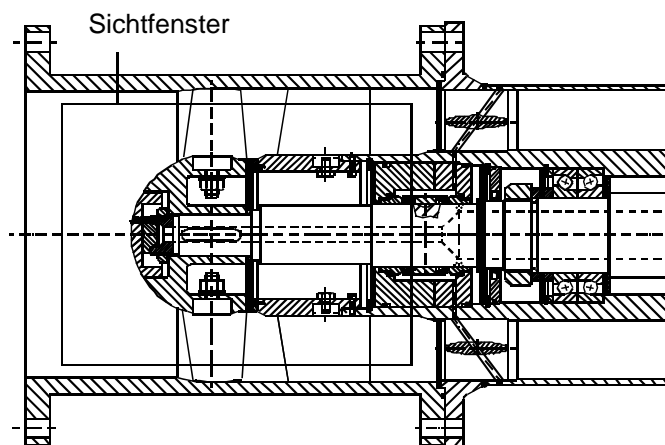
Schnittzeichnung der untersuchten Pumpe mit Sichtfenster
